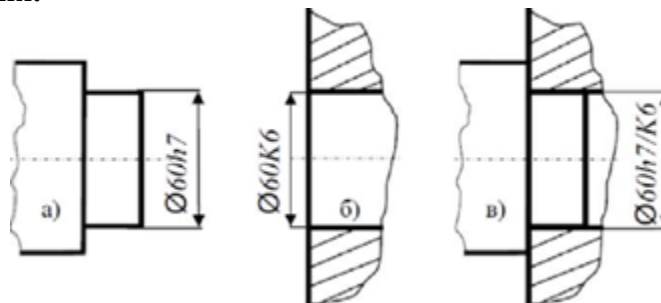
Допуск вала (а), допуск отверстия (б) и сопряжение вала с отверстием (в).
